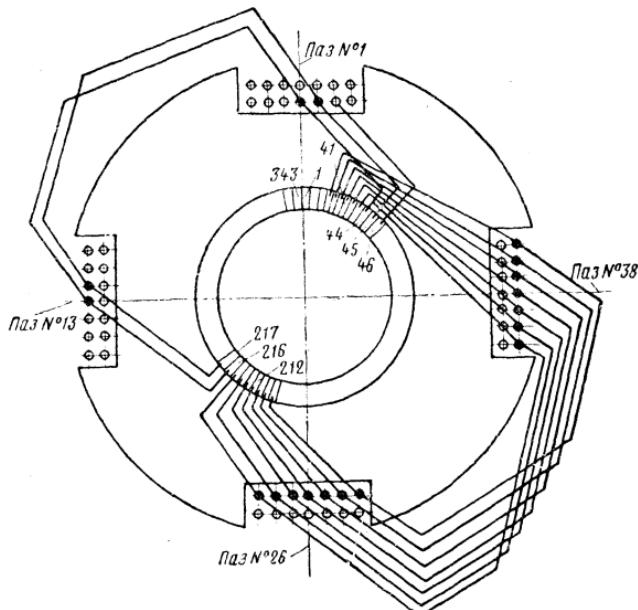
Схема соединения обмотки якоря двигателя НБ-429А с коллекторными пластинами
